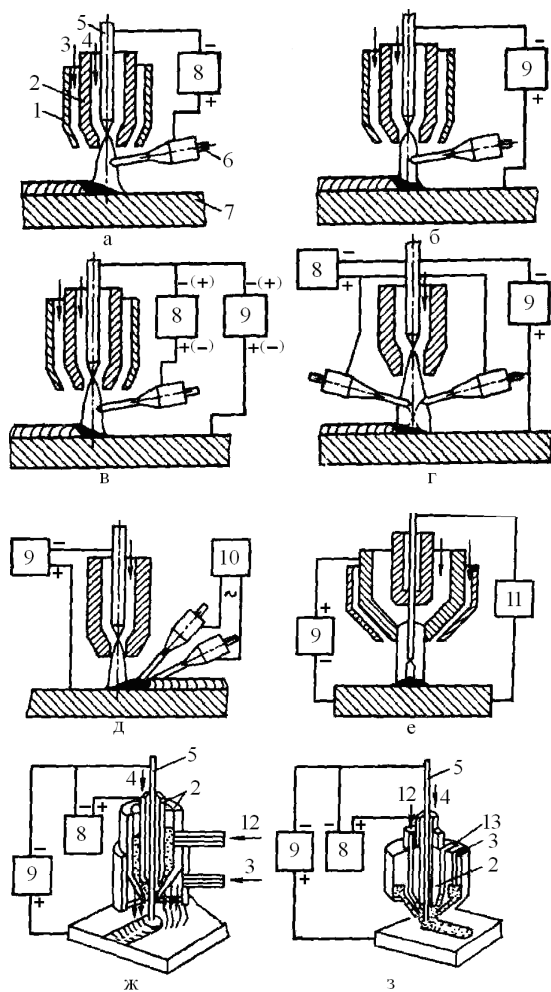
Принципові схеми процесу плазмового наплавлення[14];
